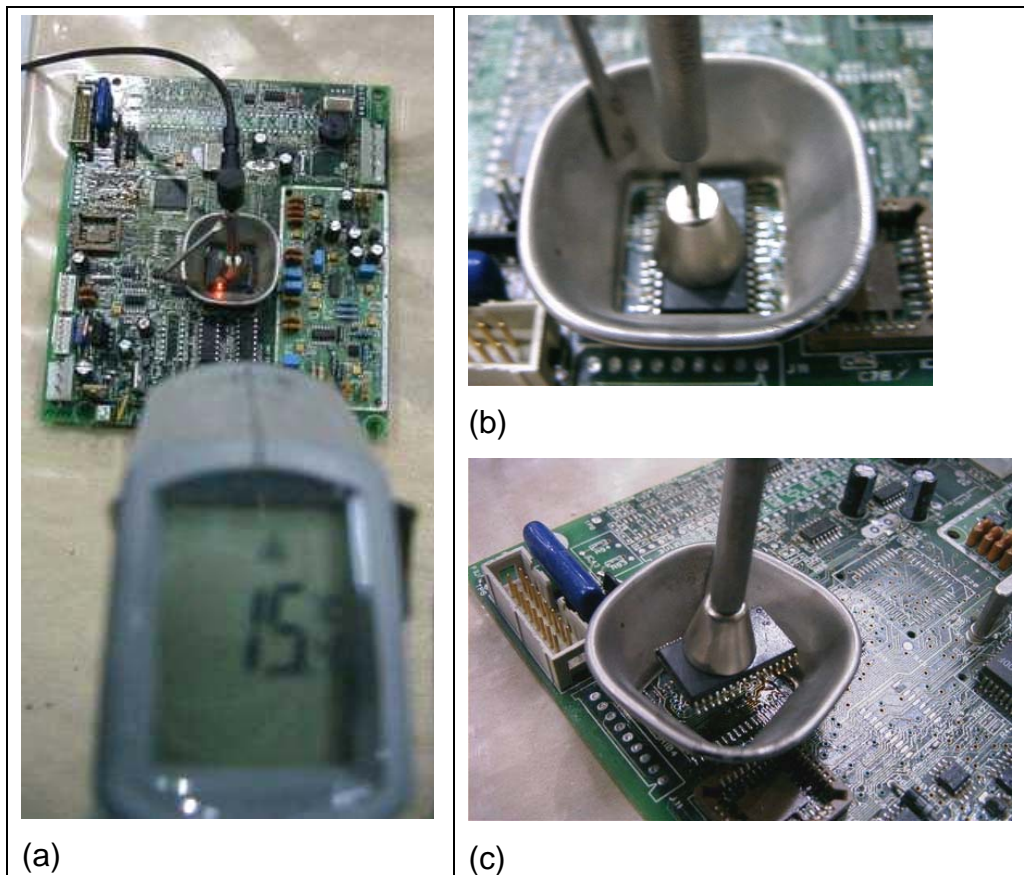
Desoldado de componentes de PCB con chorro de aire caliente.
